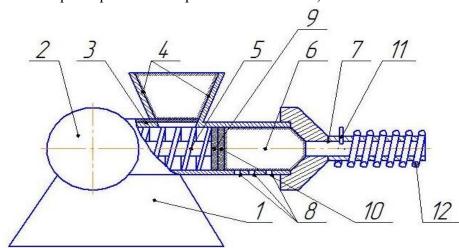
Шнековый пресс для приготовления органических брикетов из подстилочного навоза: 1 — рама, 2 — электропривод, 3 — корпус, 4 — бункер, 5 — рабочая камера со шнеком, 6 — камера прессования, 7 — насадка для формовки брикетов, 8 — дренажные отверстия, 9 — противорежущая пластина, 10 — нож, 11 — термометр, 12 — спираль для нагрева.
